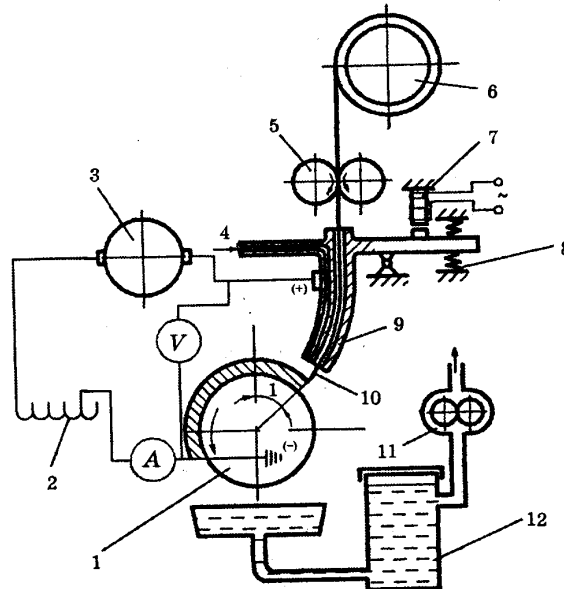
Схема установки для вібродугового напавлення деталей
